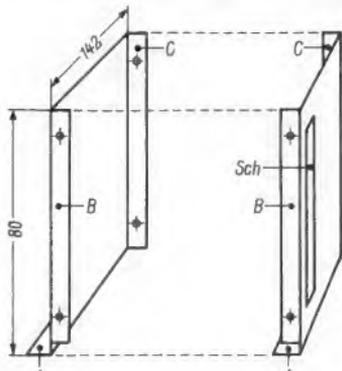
Ansicht der senkrechten Stütz- und Abschirmbleche aus halbhartem 1,5-mm-Aluminiumblech
